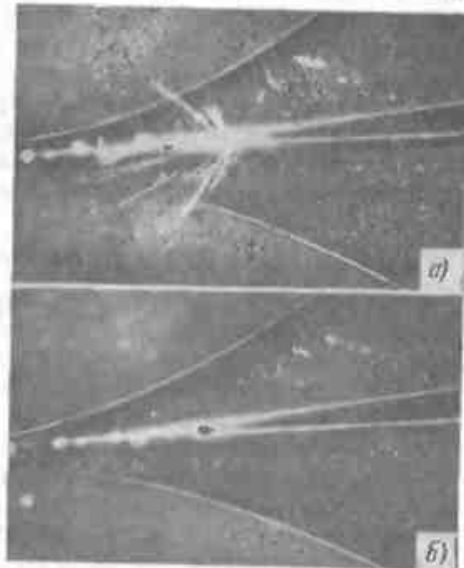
Кадры скоростной киносъемки процесса радиочастотной сварки с расплавлением металла до точки схождения кромок:
